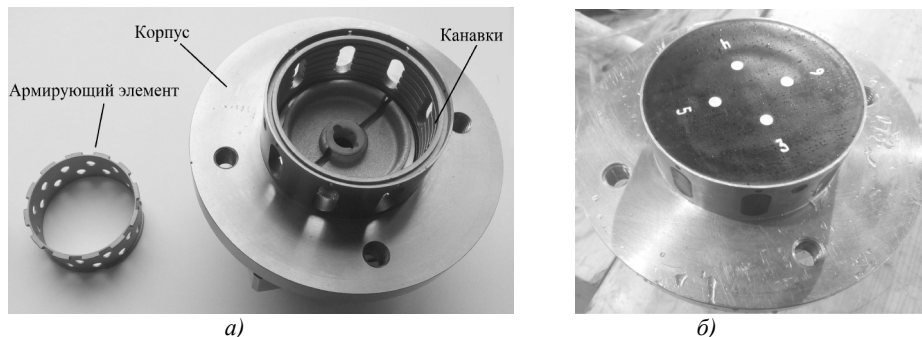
а) Детали модернизированного ГДИЛ и б) опытный образец датчика для испытаний
